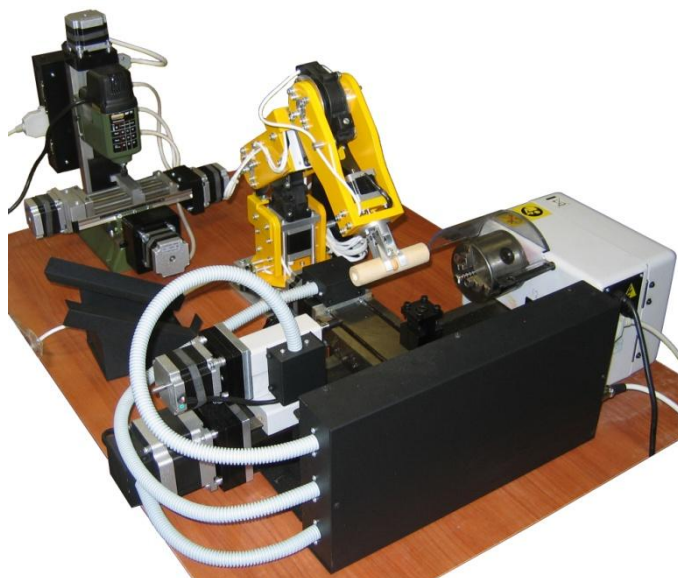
Модель ГПМ на базе токарного и фрезерного станков с компьютерным управлением
